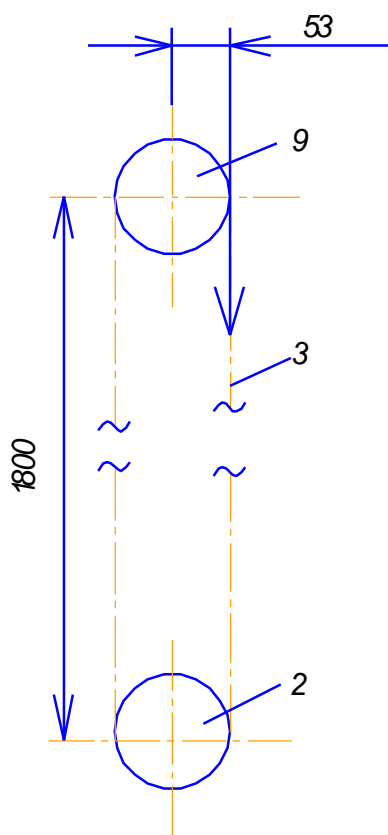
Элемент кинематической схемы звездочки с цепью
